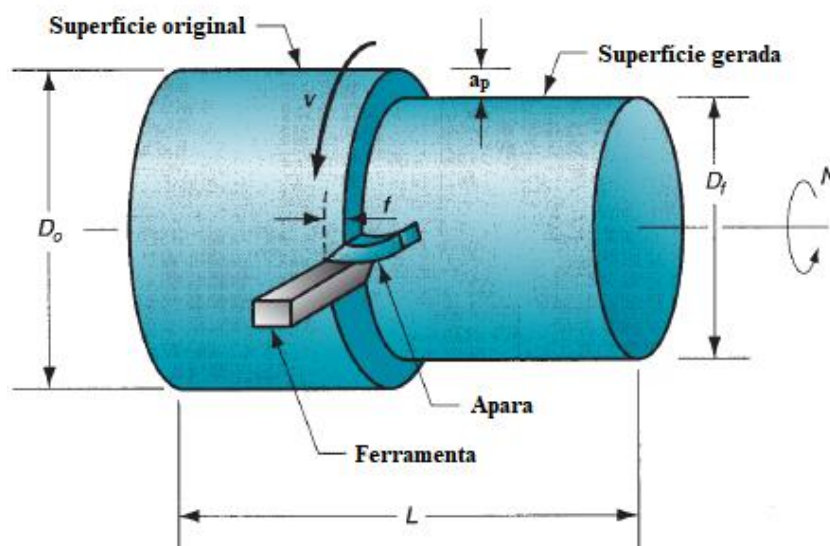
Torneamento cilíndrico (adaptado de [6])
